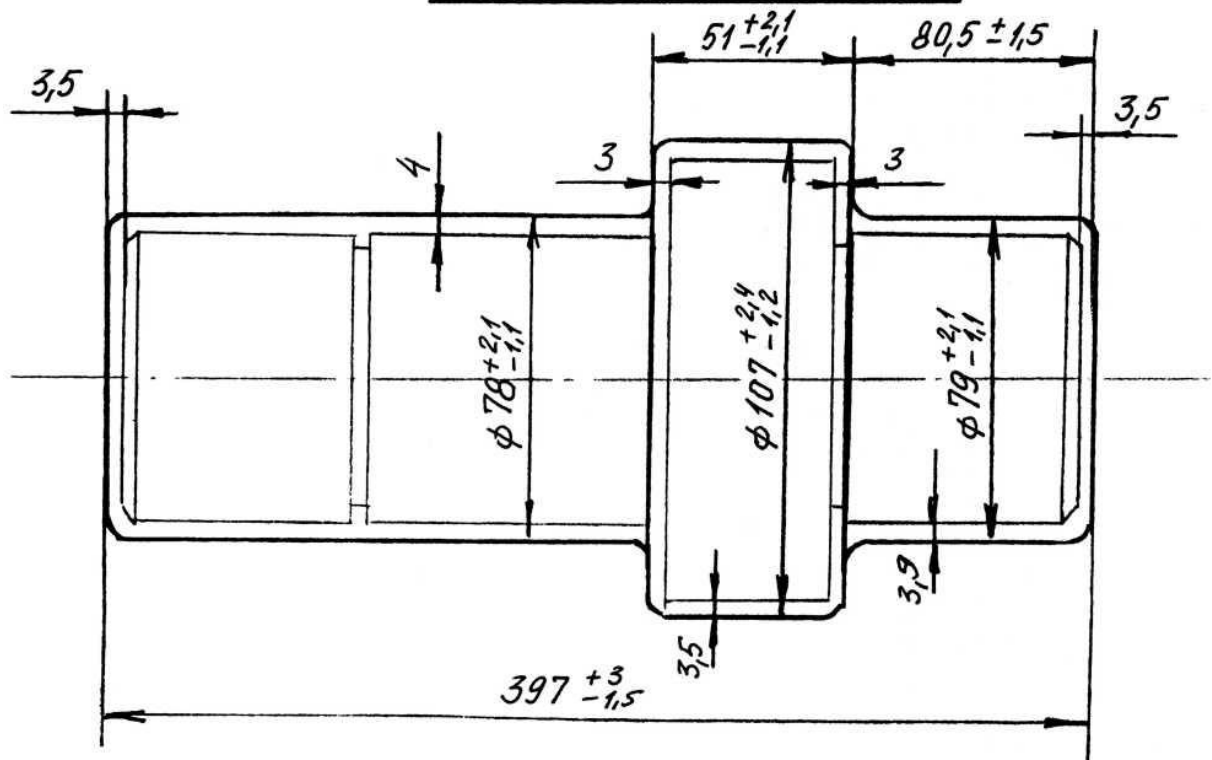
заготовка – поковка, штампованная на ГКМ.
